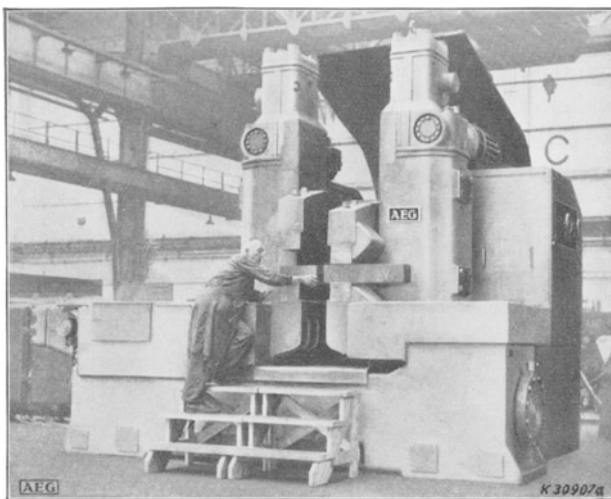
Besonders große Abbrenn-Stumpfschweißmaschine.
